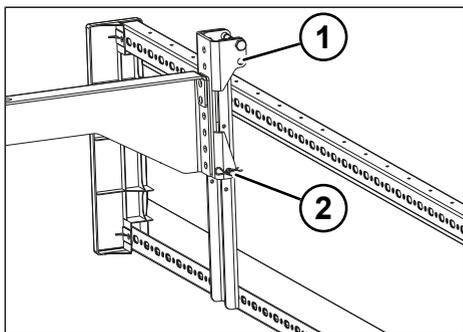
Dispositivo di protezione laterale abbassato (vista lato posteriore))
